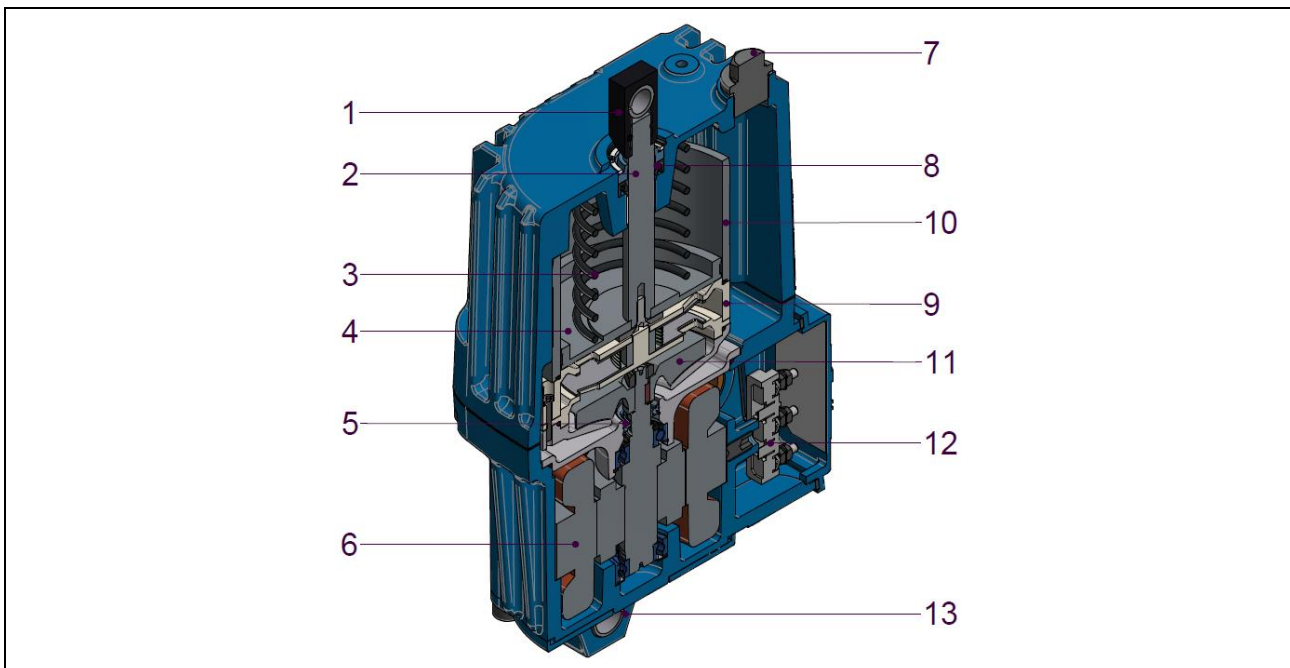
Aufbau ELDRO®-Gerät ED120 / ED220
